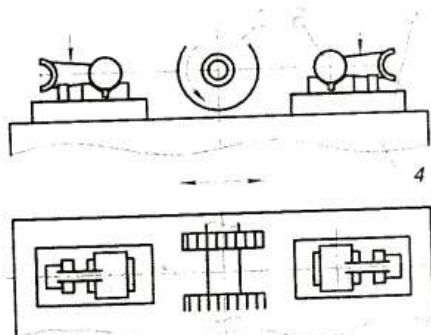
Схема маятникового фрезерування поверхнь головок
